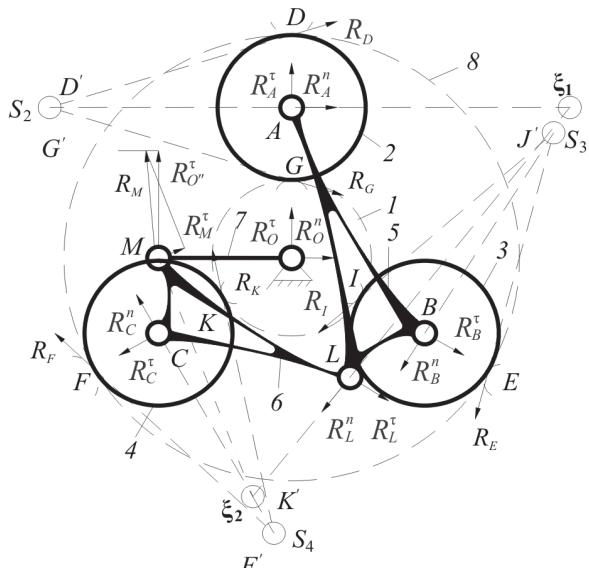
Трехсателлитная планетарная передача с дополнительными рычагами
